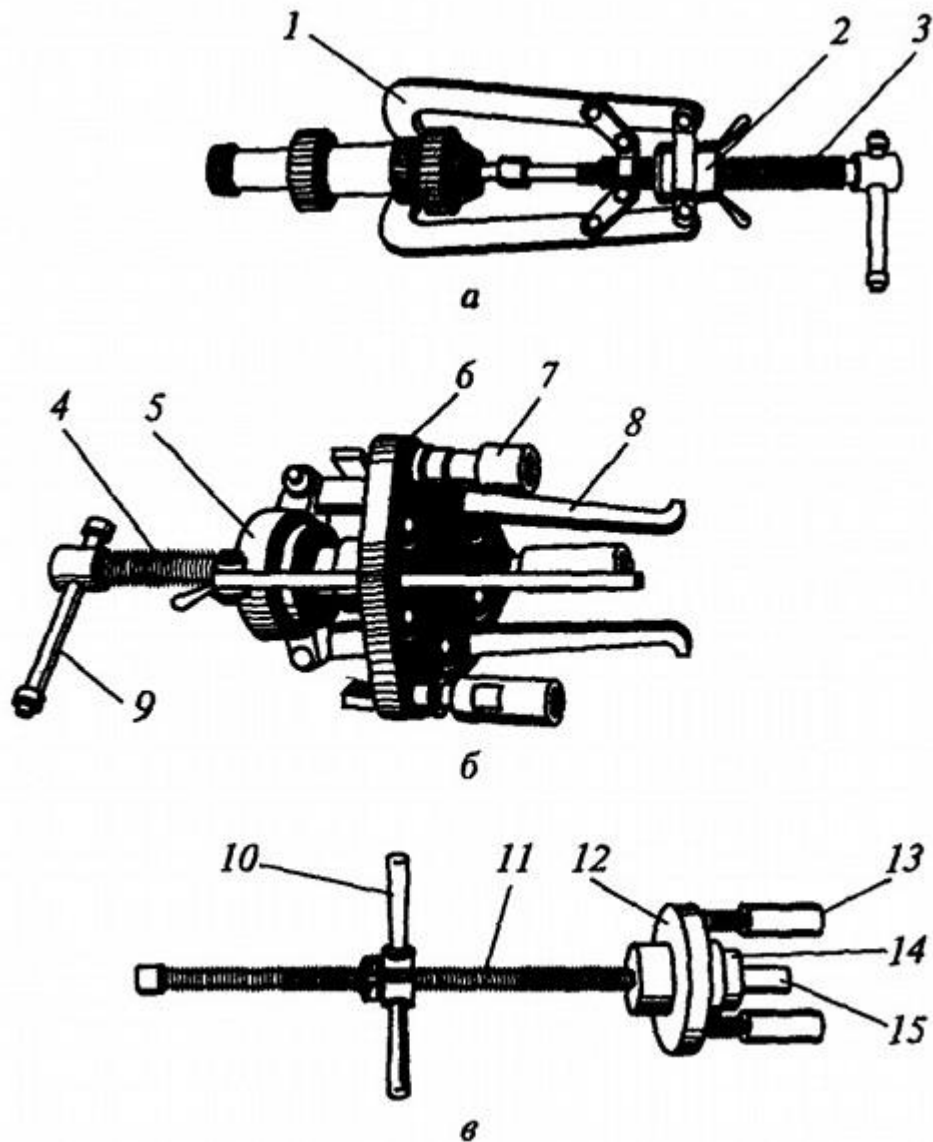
Приспособления, применяемые при разборке подшипников: а – для снятия шарикоподшипников с вала; б – для демонтажа Наружных колец конических роликоподшипников; в – для выпрессовки подшипников качения; 1 и 8 – захваты; 2, 5 и 14 – гайки; 3, 4 и 11 – винты; 6 – плита; 7 и 13 – штыри; 9 и 10 – рукоятки; 12 – диск; 15 – шайба
